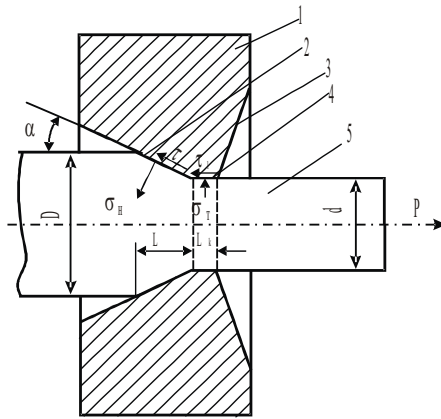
Схема процесу волочіння: 1- волока; 2- вхідний конус; 3- вихідна розпушка; 4 - пасок, що калібрує; 5 – поволока; (Р - сила волочіння; D – вихідний дріт; d – діаметр дроту після волочіння; α напівкут вхідного (робітника) конуса волоки; l - довжина ділянки вогнища деформації; l_k - довжина паска, що калібрує; σ_n - напруга волочіння
